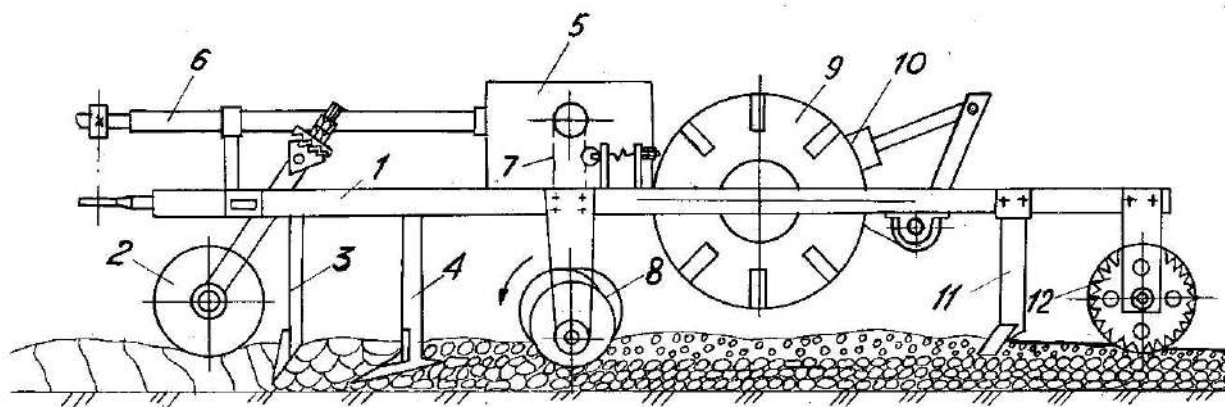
Технологическая схема орудия комбинированного типа: 1 – рама; 2 – опорный каток; 3 – рыхлительная лапа; 4 – культиваторная лапа; 5 – редуктор; 6 – карданный вал; 7 – цепная передача; 8 – дискователь; 9 – транспортный ход; 10 – гидроцилиндр; 11 – планировочная секция; 12 – кольчато-шпоровый каток.
